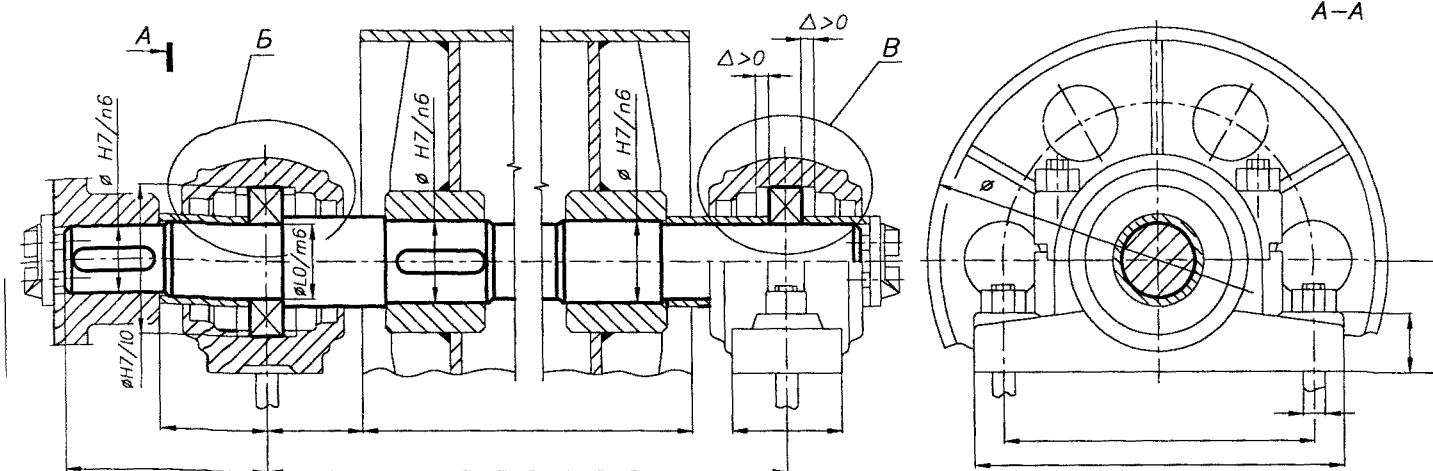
Подшипниковые узлы приводного вала барабана
